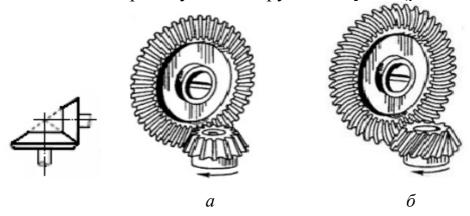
Конические зубчатые передачи: a – прямозубая; δ – с круговым зубом
